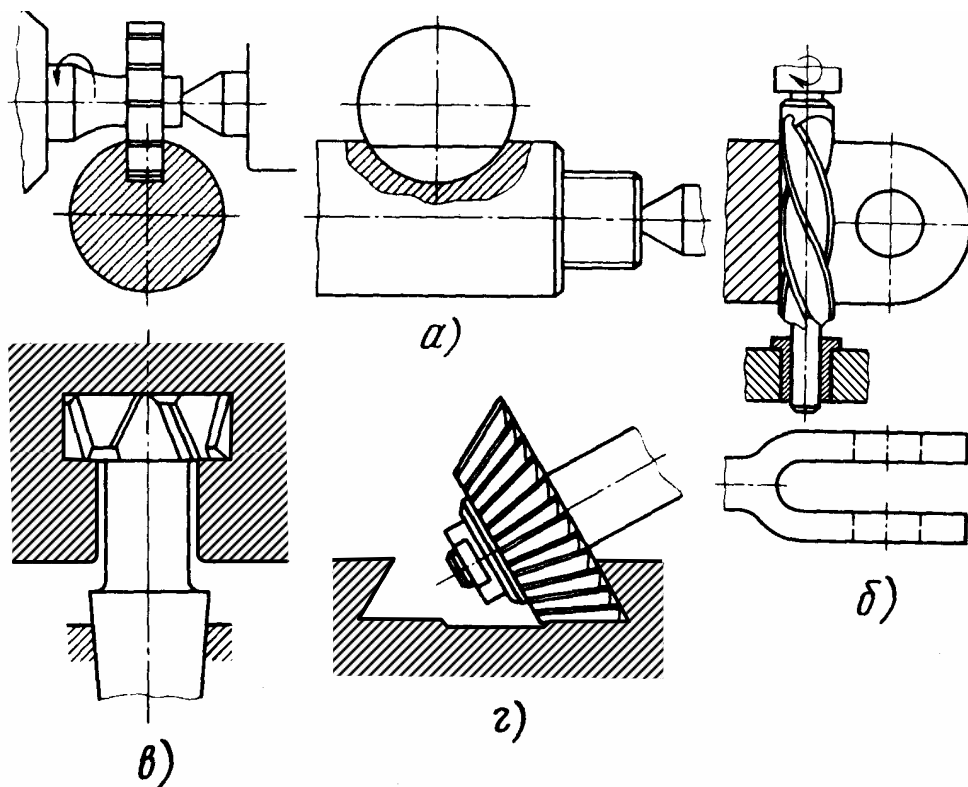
Схеми фрезерування: а – паза під сегментну шпонку; б – вушка кінцевою фрезою; в – Т-подібного паза грибковою фрезою; г – паза типу „ластівчин хвіст” кутовою фрезою
